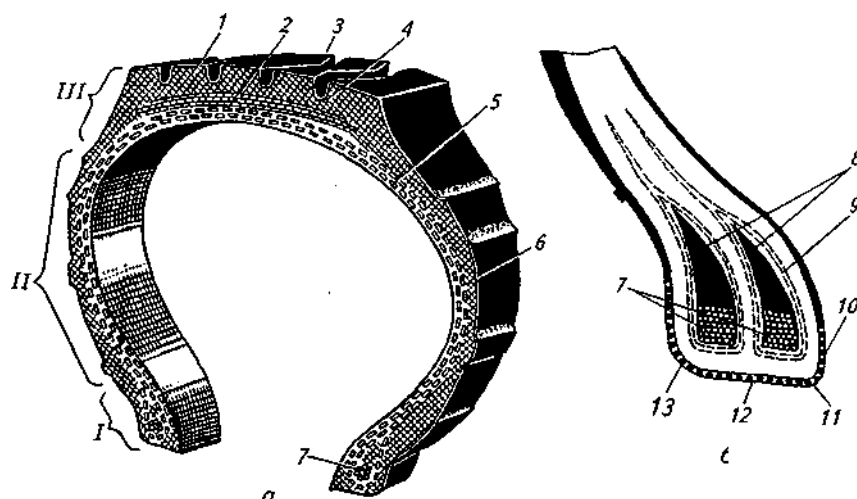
Конструкция покрышки (а) и ее борта (б): I- борт; II - боковая стенка; III - плечевая зона протектора; 1 – протектор; 2 – брекер; 3 – рисунок протектора; 4 – подканавочный слой; 5 – каркас; 6 – боковина; 7 – бортовое кольцо; 8 – наполнительные шнуры; 9 – крыло борта; 10 – бортовая лента; 11 – носок борта; 12 – основание борта; 13 – пятка борта
